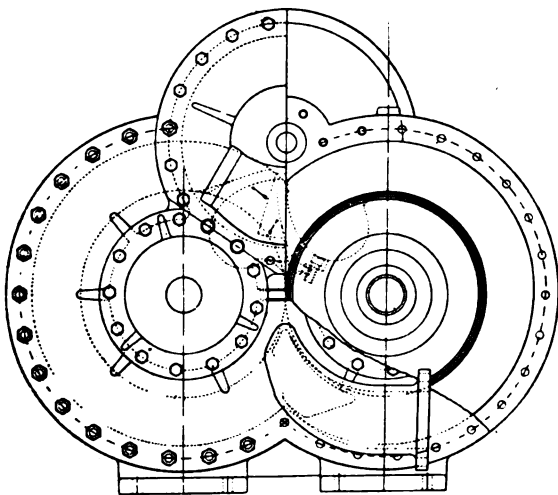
Machine rotative équilibrée Herrick, type à double piston.
